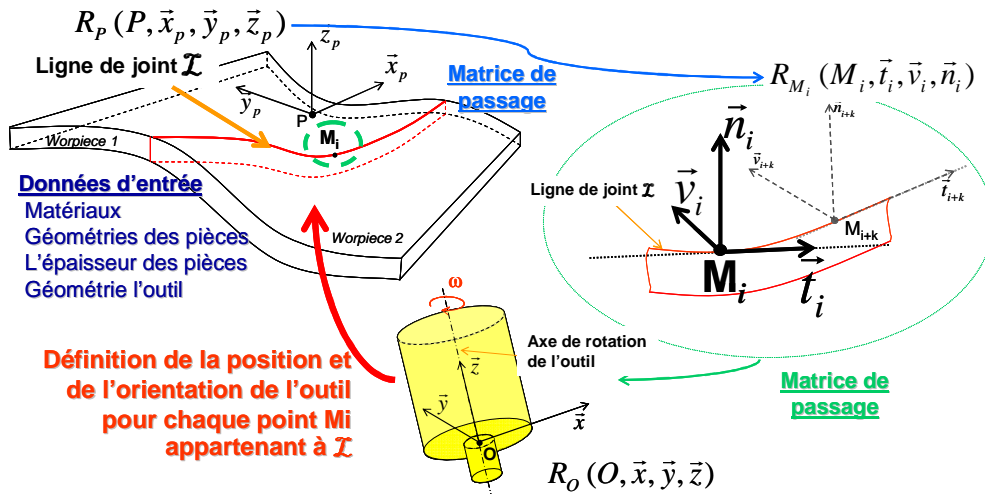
Définition de la position et l'orientation de l'outil en chaque lieu de soudure.
